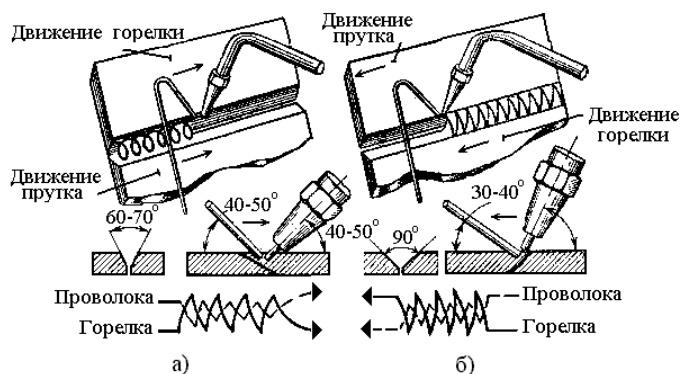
Способы газовой сварки: а) – правый; б) – левый
